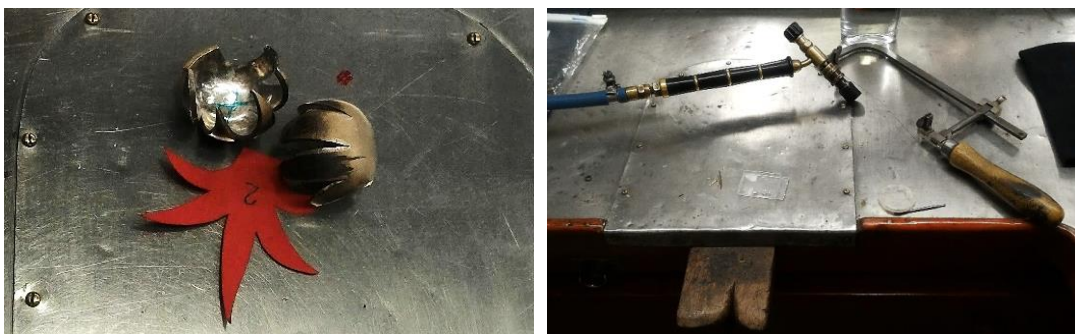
À esquerda: exemplo de modelo recortado e trabalhado de acordo com o molde; À direita: maçarico de soldadura ou maçarico brasileiro (esquerda) e serra de ourives (direita).
